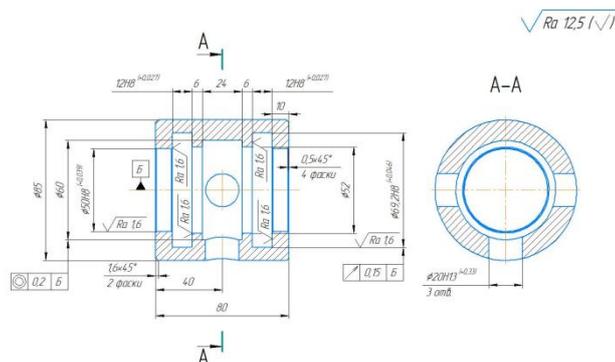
Рабочий чертеж детали «Корпус муфты»
